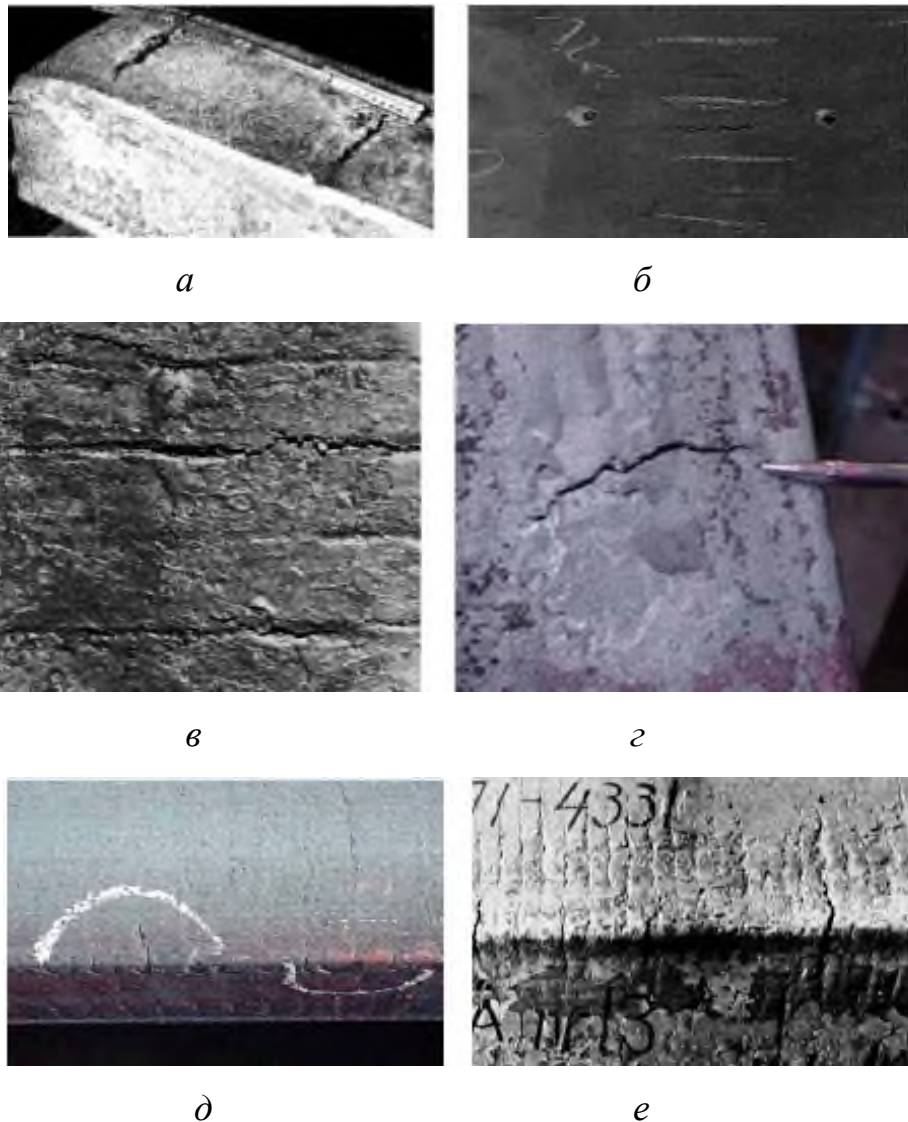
Поперечні поверхневі тріщини на межі сортової безперервнолитої заготовки (*a, б*) і сляба (*в, г*), а також на кутових ділянках (*д, е*)
